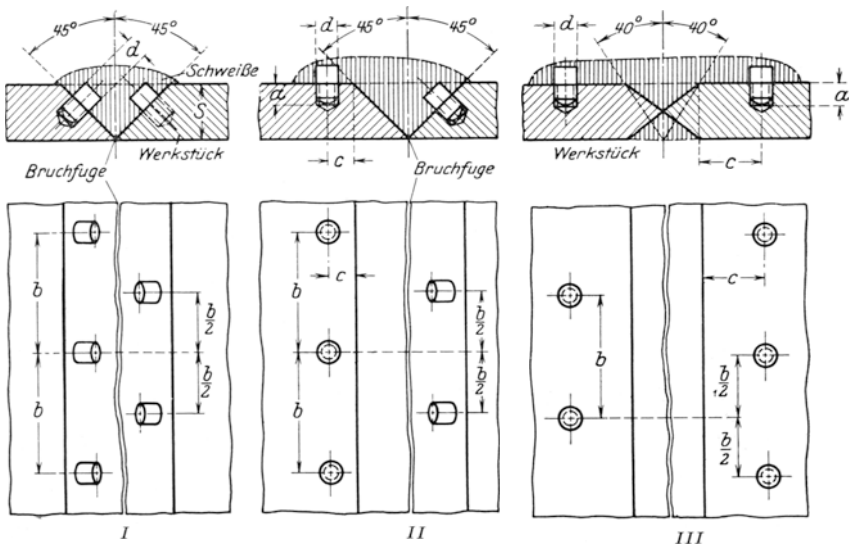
Anordnung von Stiften bei Gußeisenkalterschweißungen.
